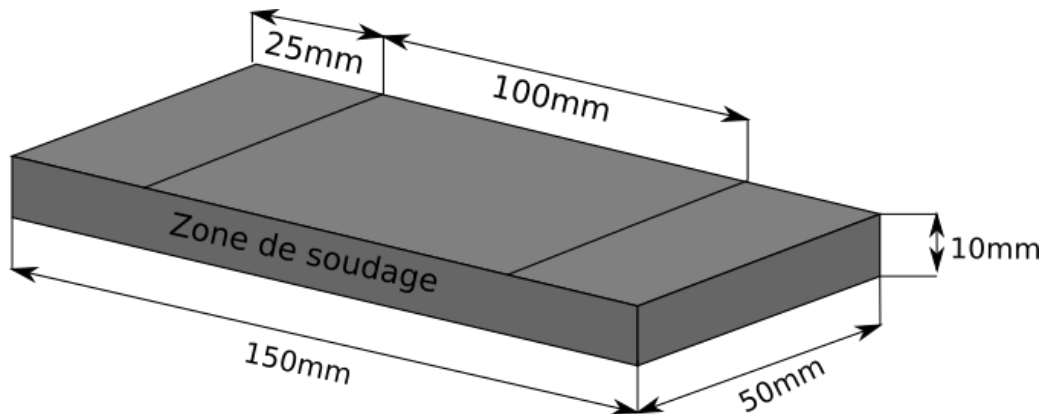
Présentation de la maquette, géométrie de la plaque soudée ainsi que la représentation de la zone de soudage.
